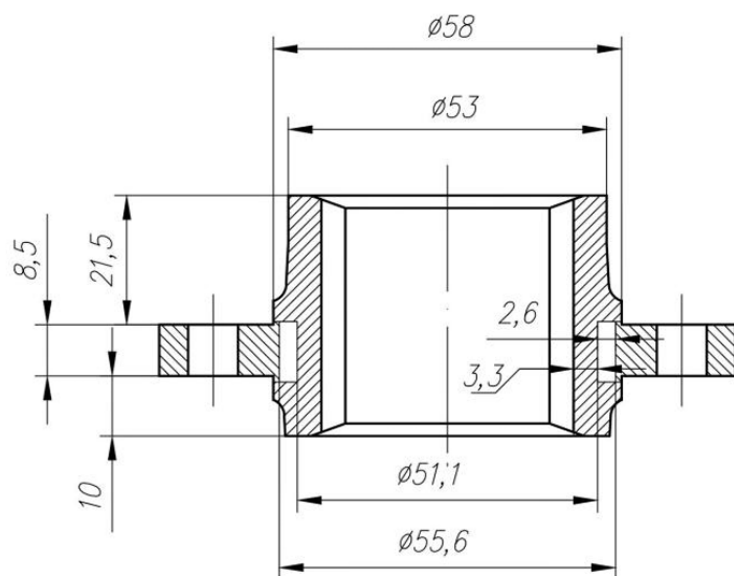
Эскиз детали «ступица» диска сцепления автомобиля
